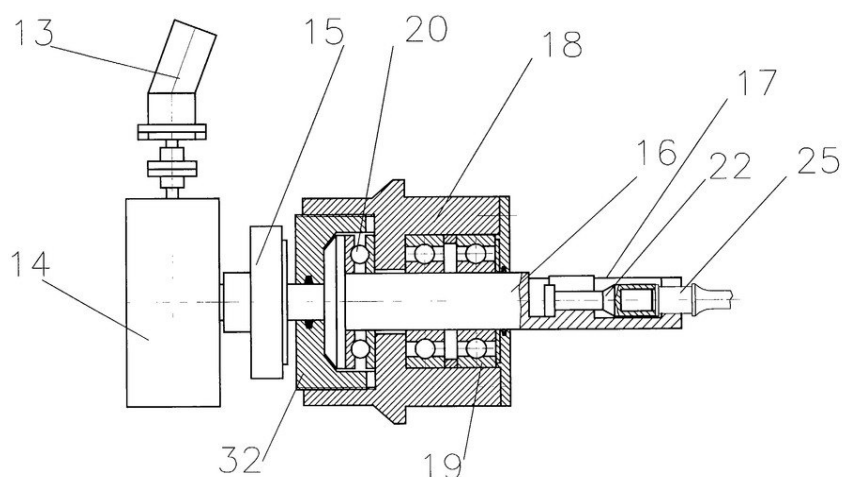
Захват для штанги в частичном разрезе, вид сбоку
